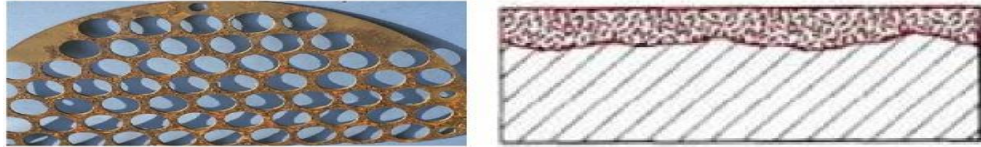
Corrosion uniforme d'une chicane en acier [2].
